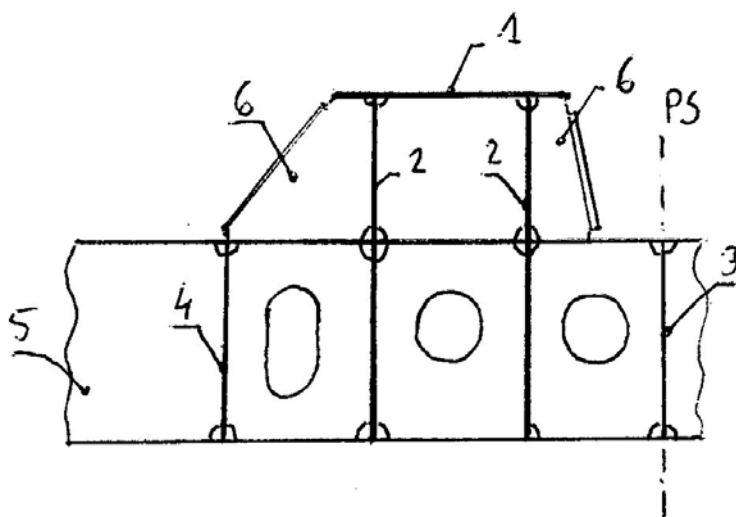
Przykładowa konstrukcja fundamentu
